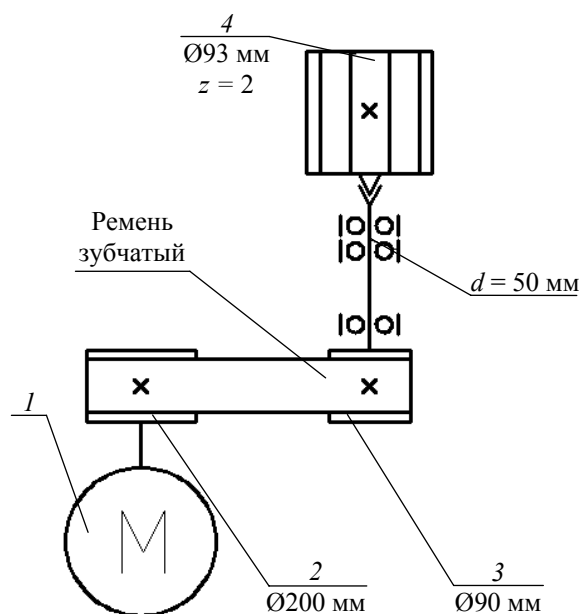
Расчетная схема привода правого вертикального фрезерного шпинделя станка Unimat 23 EL
